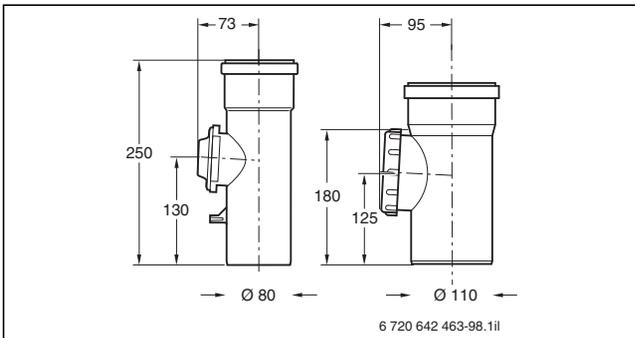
Rohr mit Prüföffnung (Maße in mm)
